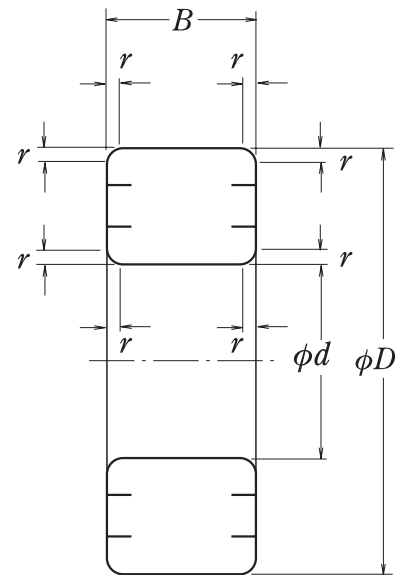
Dimensioni di ingombro dei cuscinetti radiali
